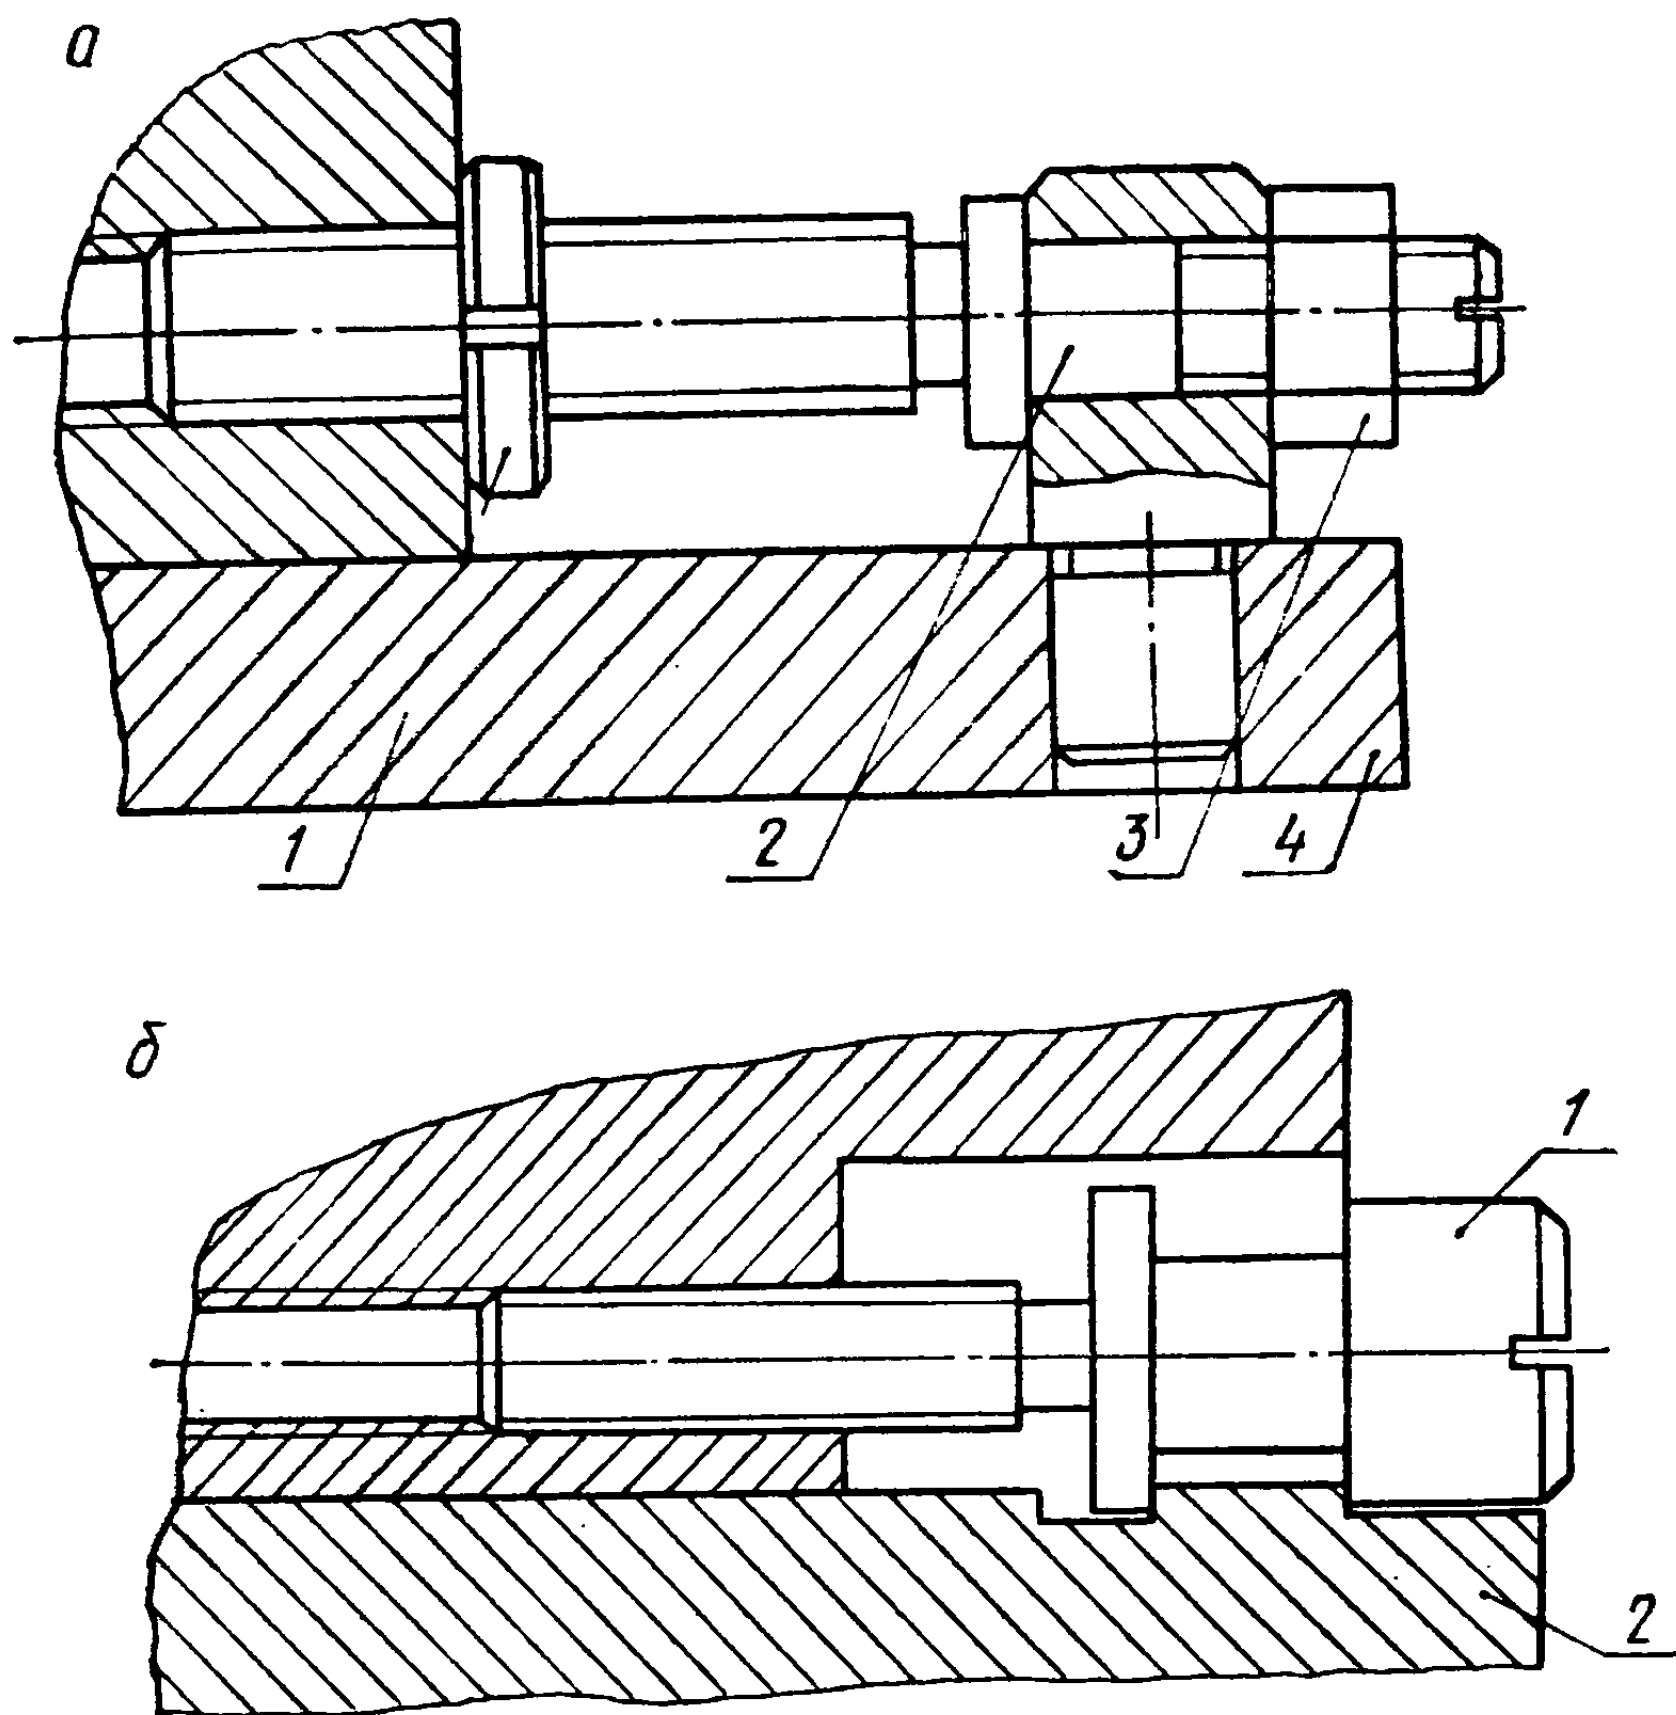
Основные способы регулирования зазоров в фрезерных станках.
